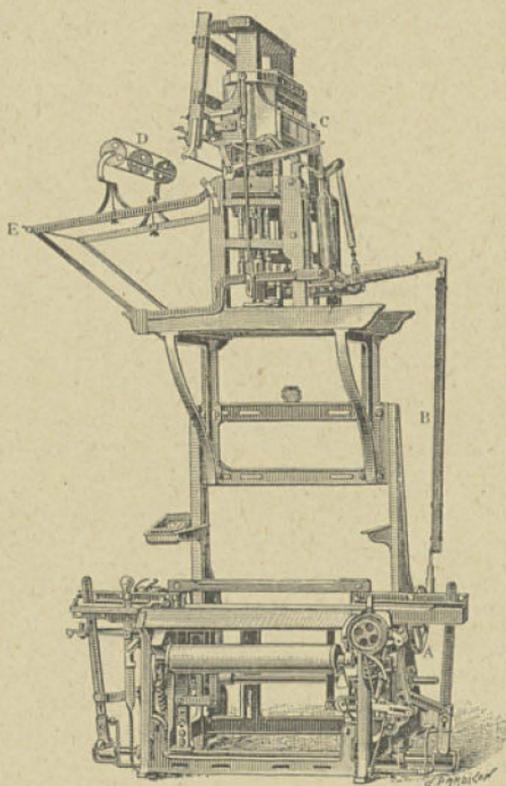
Vue d'ensemble d'un métier à mécanique Jacquard.
